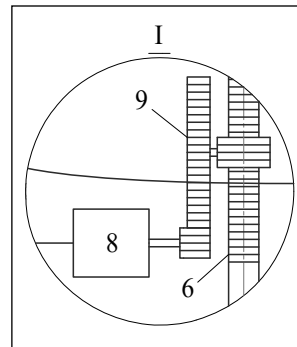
Електромеханічний регулятор (виноска I рис. 1): 6 — шток; 8 — електродвигун; 9 — редуктор.
